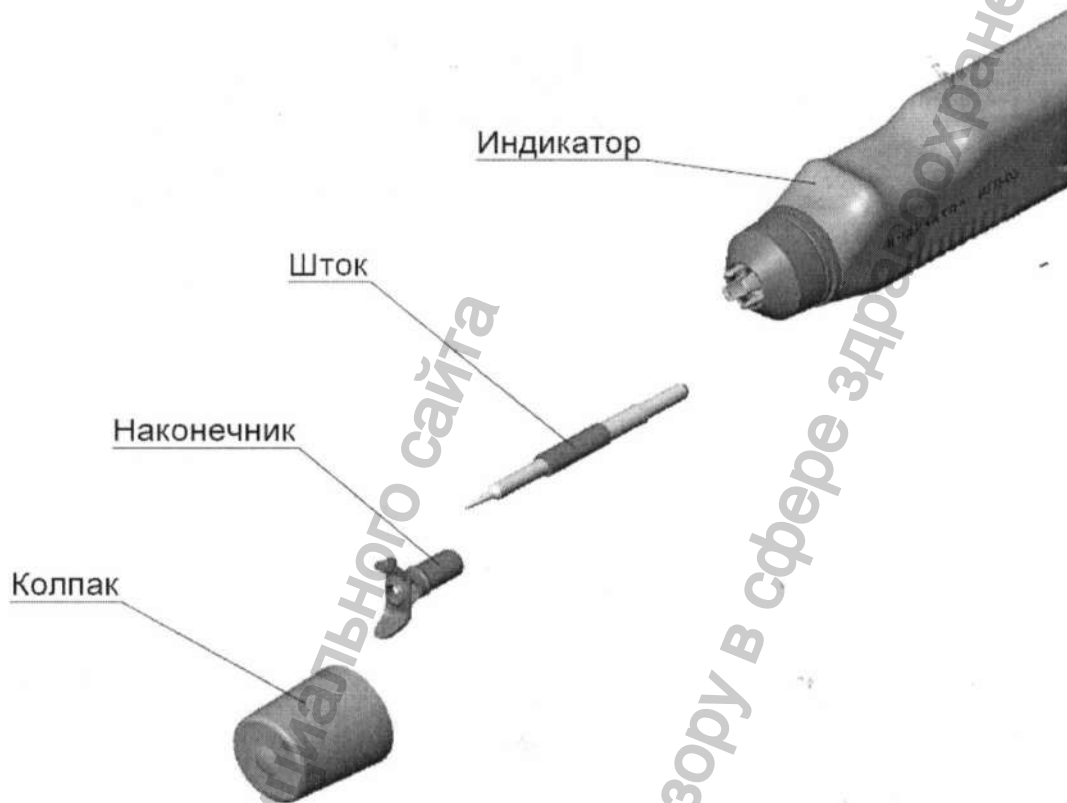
Подготовка индикатора к очистке штокового механизма
